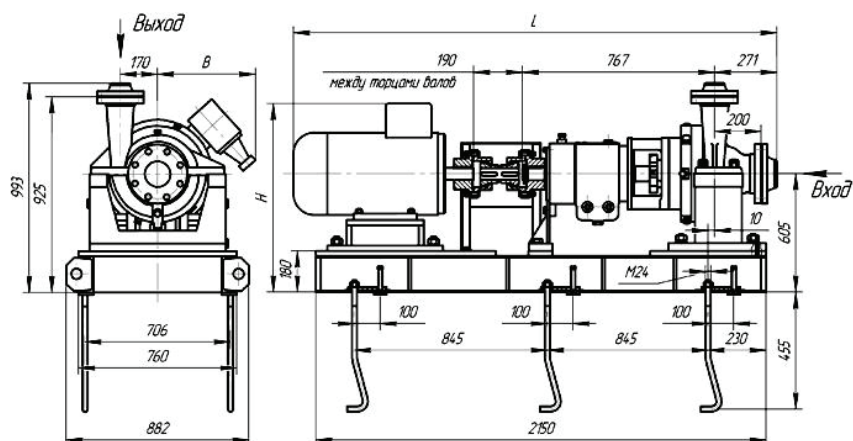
Габаритные и присоединительные размеры насосов НК-210/80 [5]
